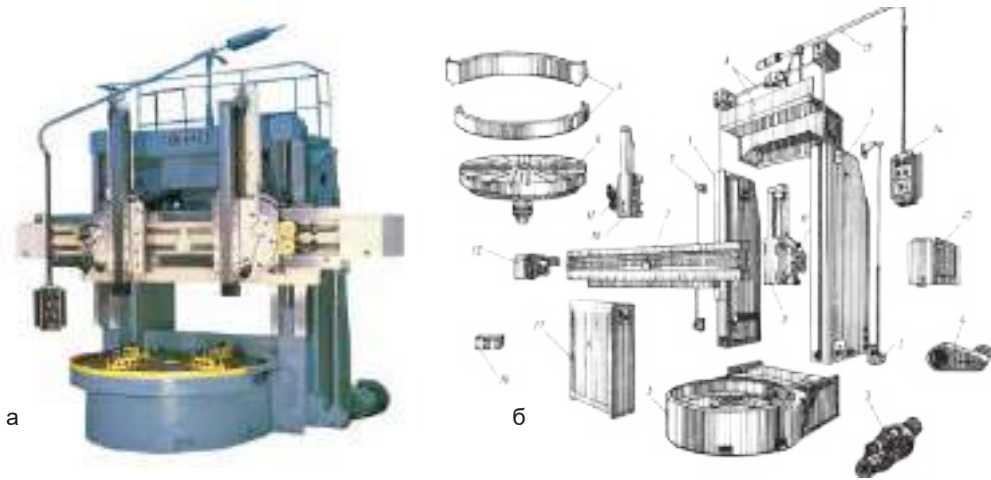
Двостояковий токарно-карусельний верстат моделі 1Л532: а — загальний вигляд верстата; б — розташування основних частин верстата:
